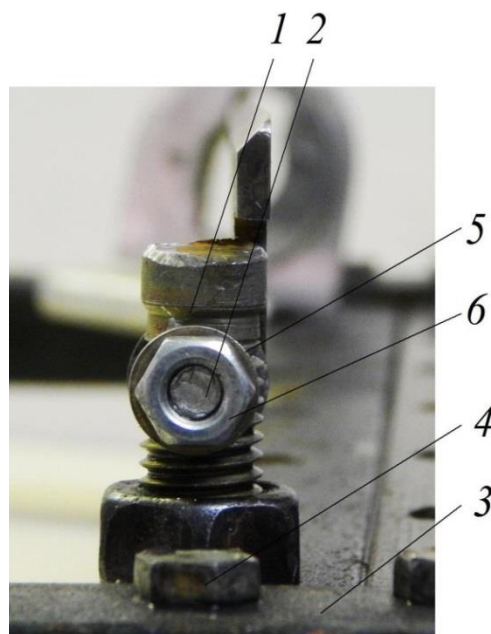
Регулировочный кронштейн: 1 – болт; 2 – шпилька;
